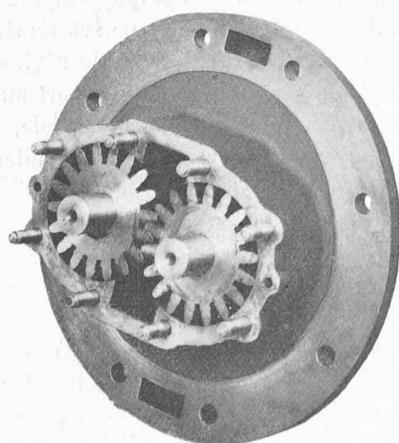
Pompe à engrenages destinée aux petits régulateurs.
